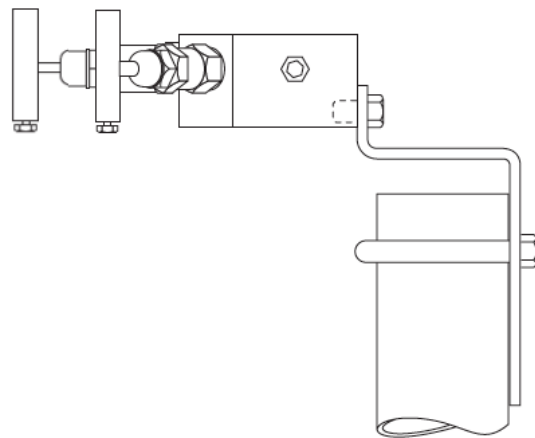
Montagem Típica do Bloco Manifold MB3 com Suporte - AM
